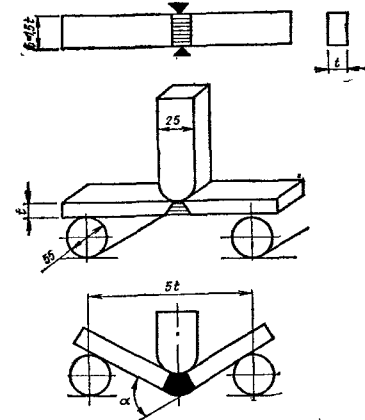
Испытание наплавленного металла на изгиб для определения прочности и пластичности
